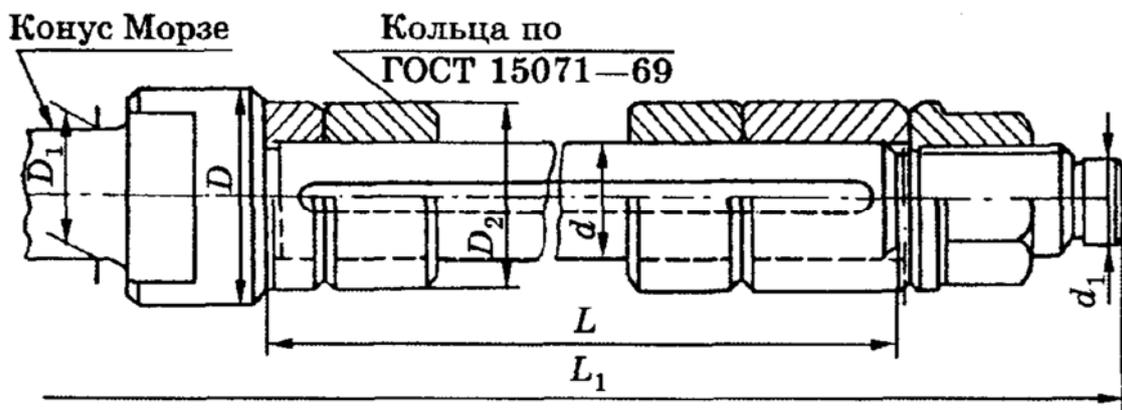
Оправка для крепления дисковых и цилиндрических фрез с передачей крутящего момента при помощи продольной шпонки
